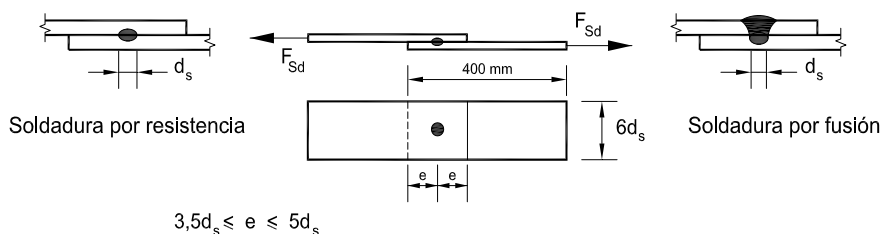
Probeta para ensaio de soldadura por puntos
